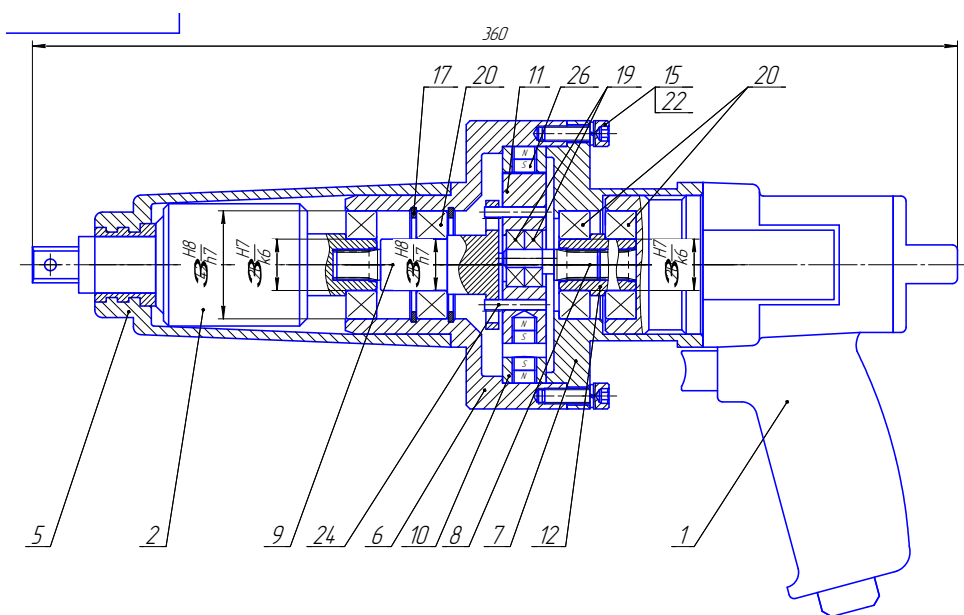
Гайковерт ударного действия с магнитным редуктором (поз. 11)
